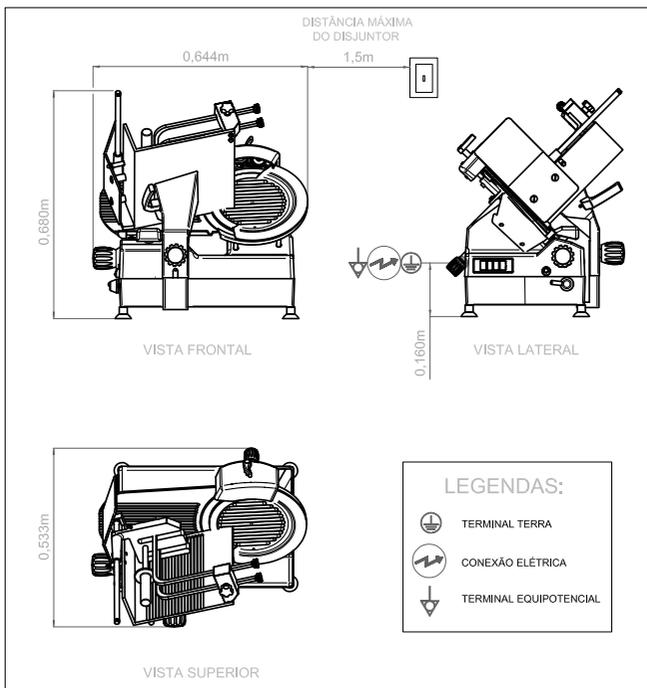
Dimensões Gerais e Instalação - Fatiador de frios automático HCA30
